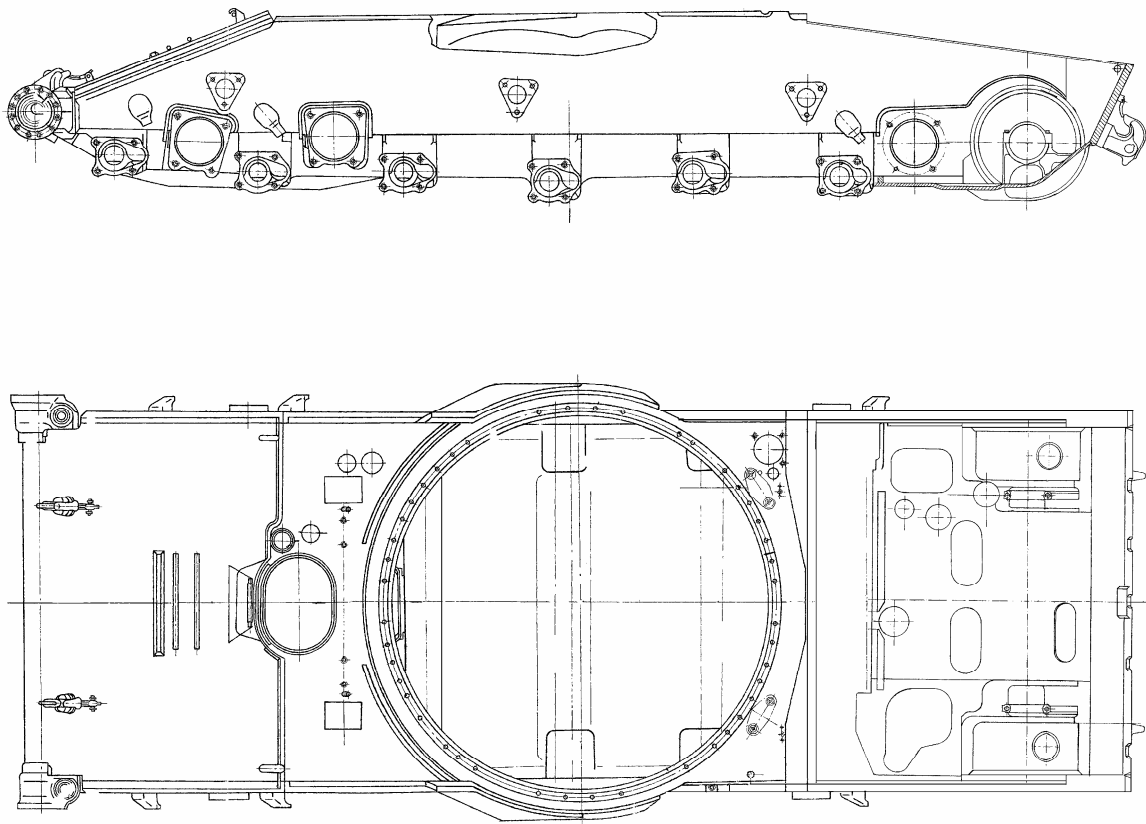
Корпус танка Т-72 после доработки под установку двигателя 5ТДФМА
